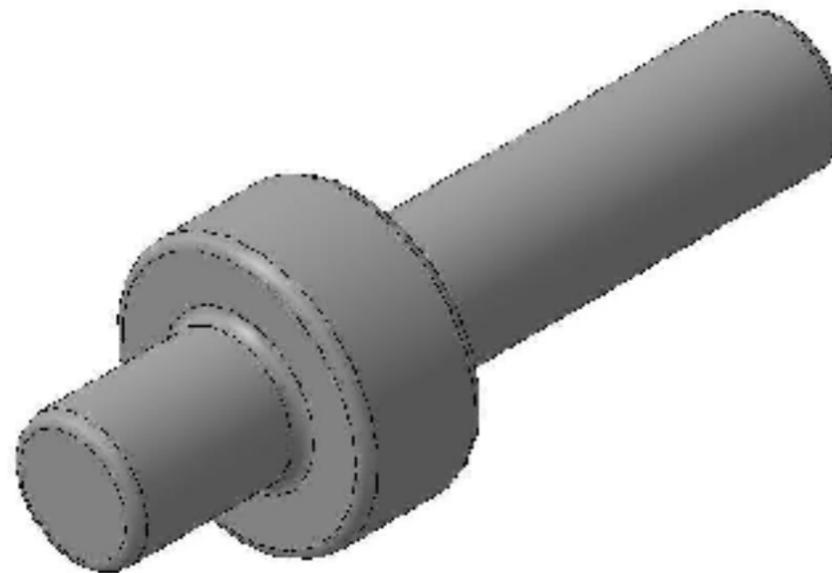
3D-модель заготовки при штампуванні на КГШП (З)
